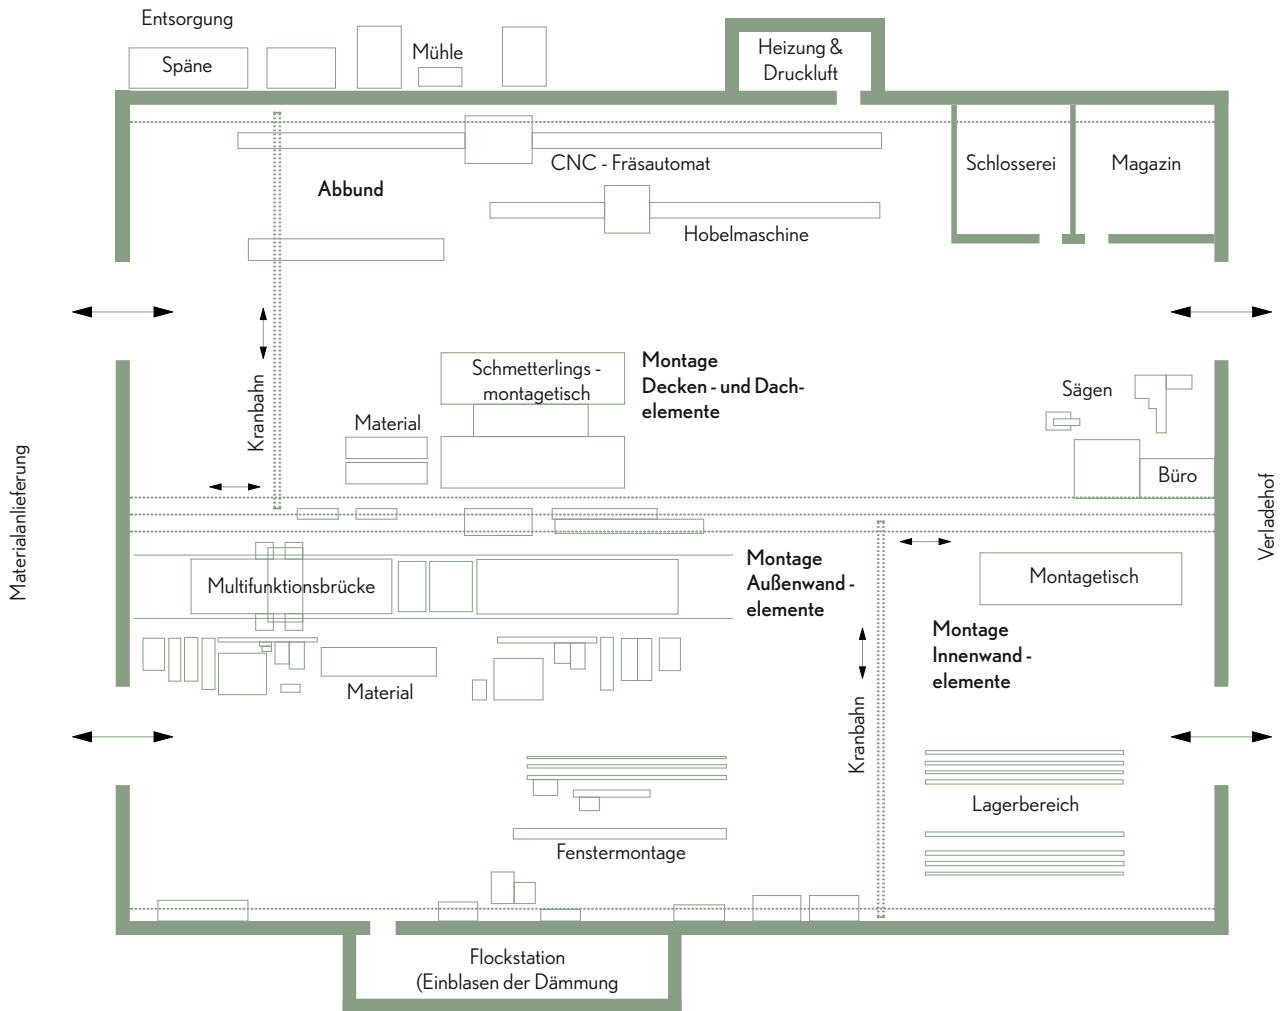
| Produktionsablauf im Werk, beispielhafter Grundriss Werkhalle, Holzbaununternehmen Gump & Maier, Binswangen (DE)
